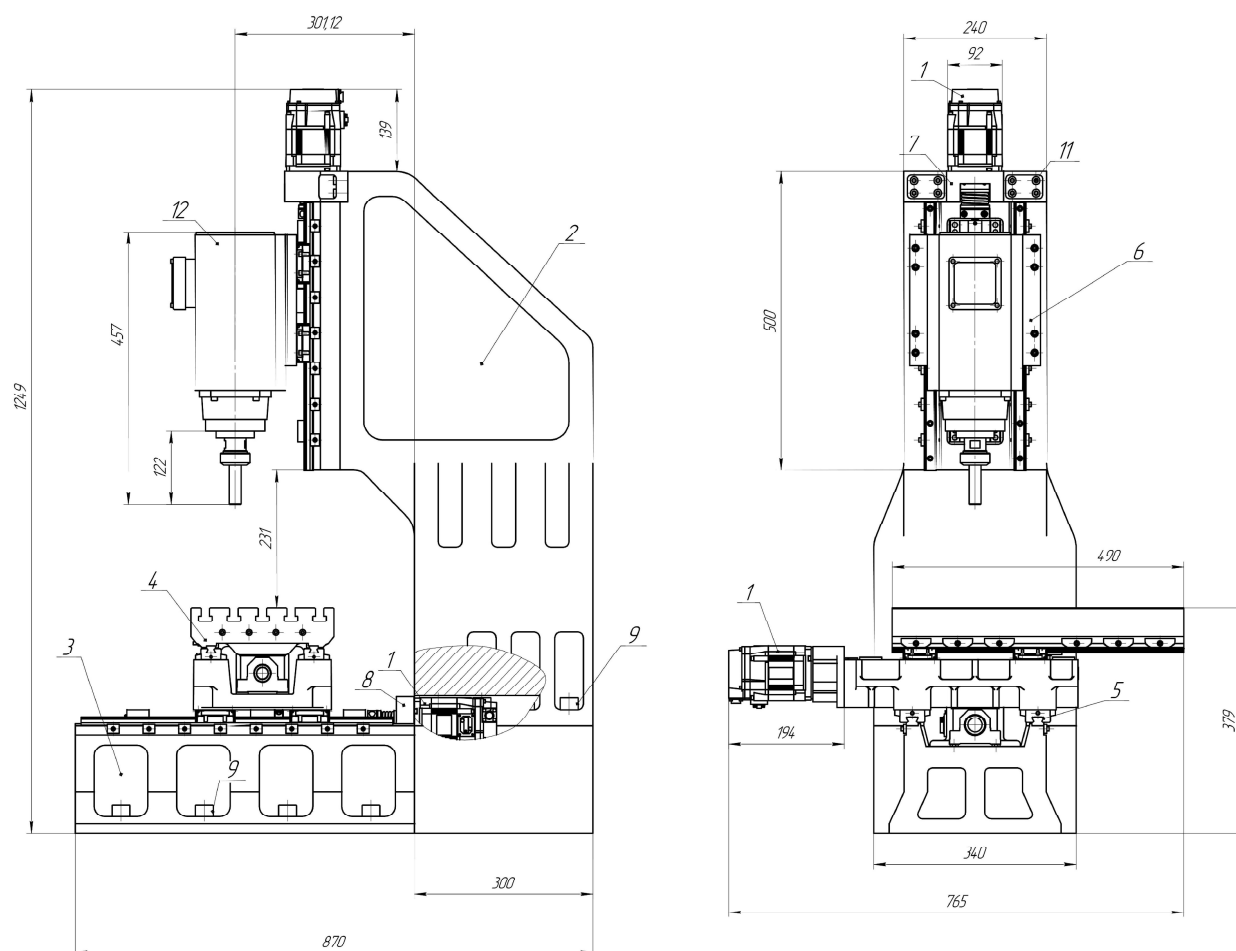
Вертикально-фрезерний верстат мод. 6P13
